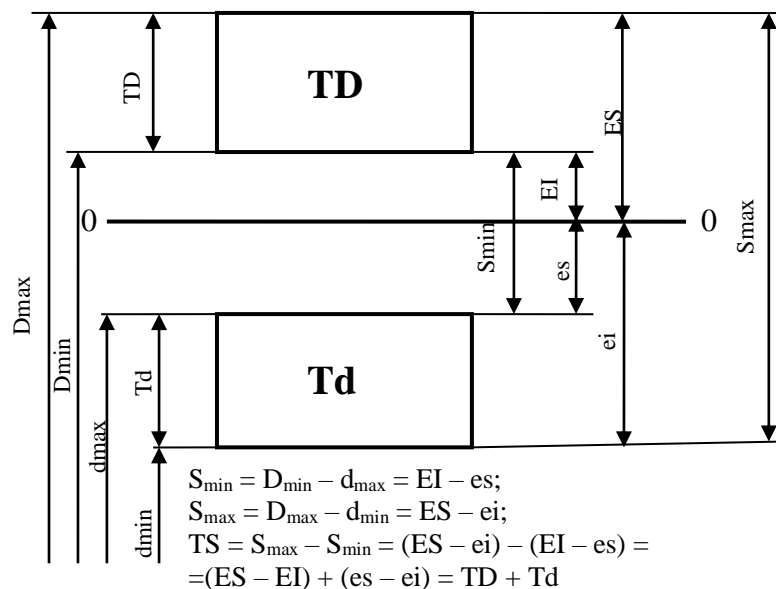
Схема расположения полей допусков при посадке с зазором
